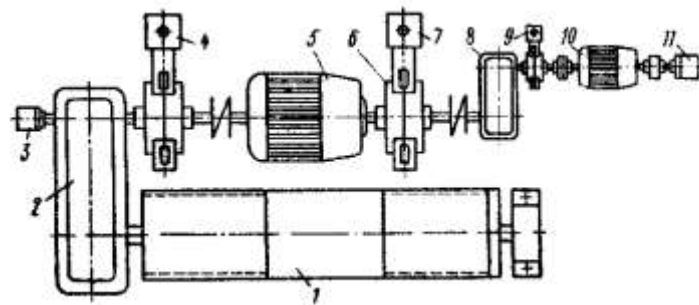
Схема многоскоростного механизма подъема с планетарной муфтой
